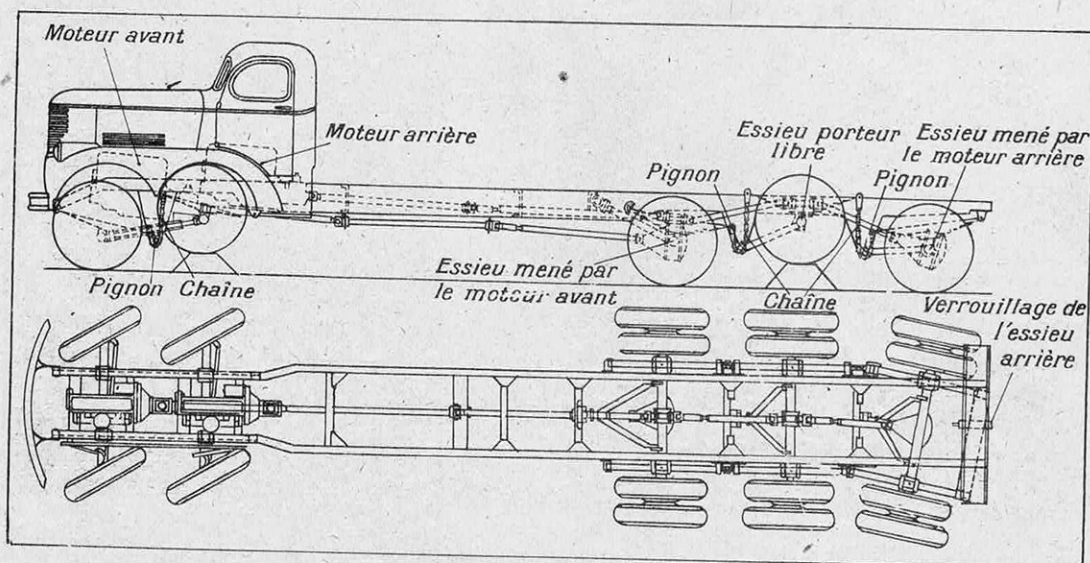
UN CAMION DE 20 T A DEUX MOTEURS ET SEIZE ROUES (EISENHAUER MANUFACTURING CO)
